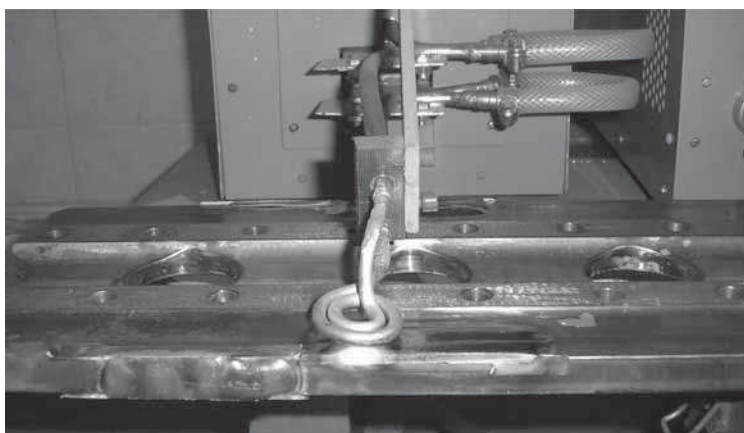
ЛТО наплавлення на плоских поверхнях рейки
